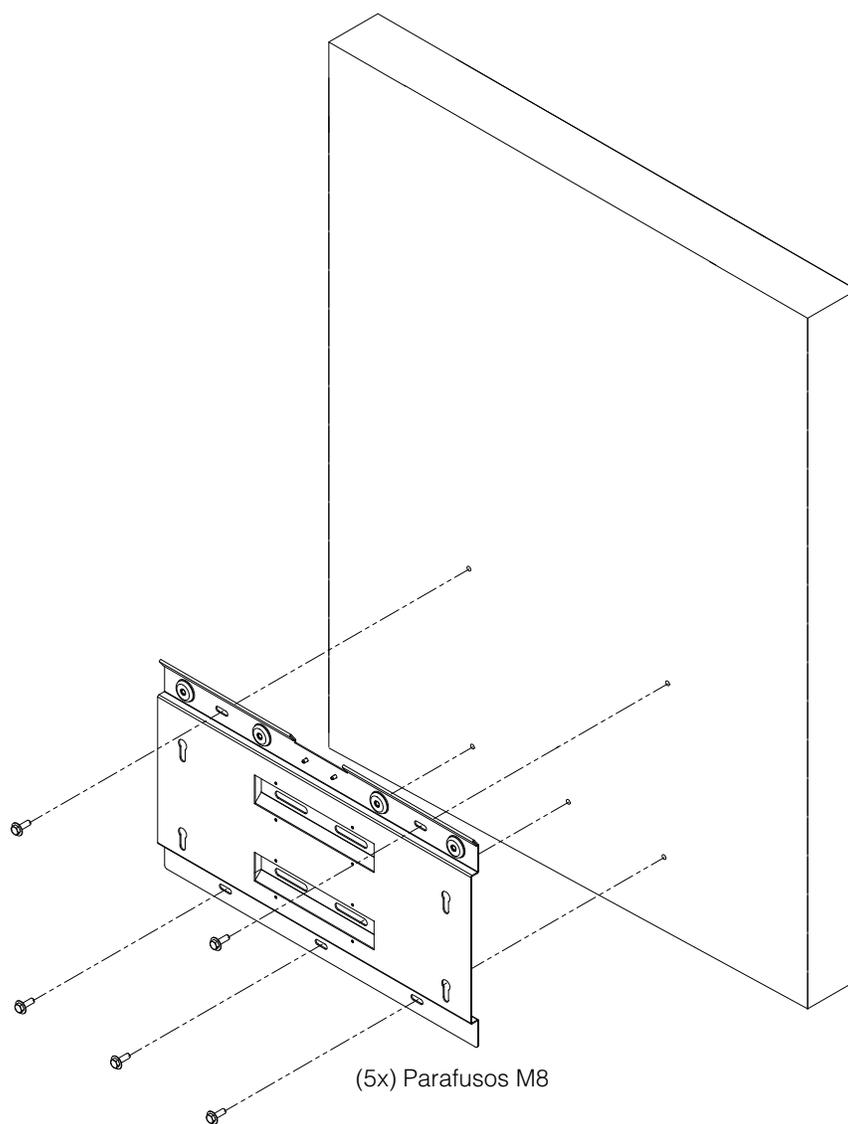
Fixação da placa de fixação da caixa de ligações na parede
